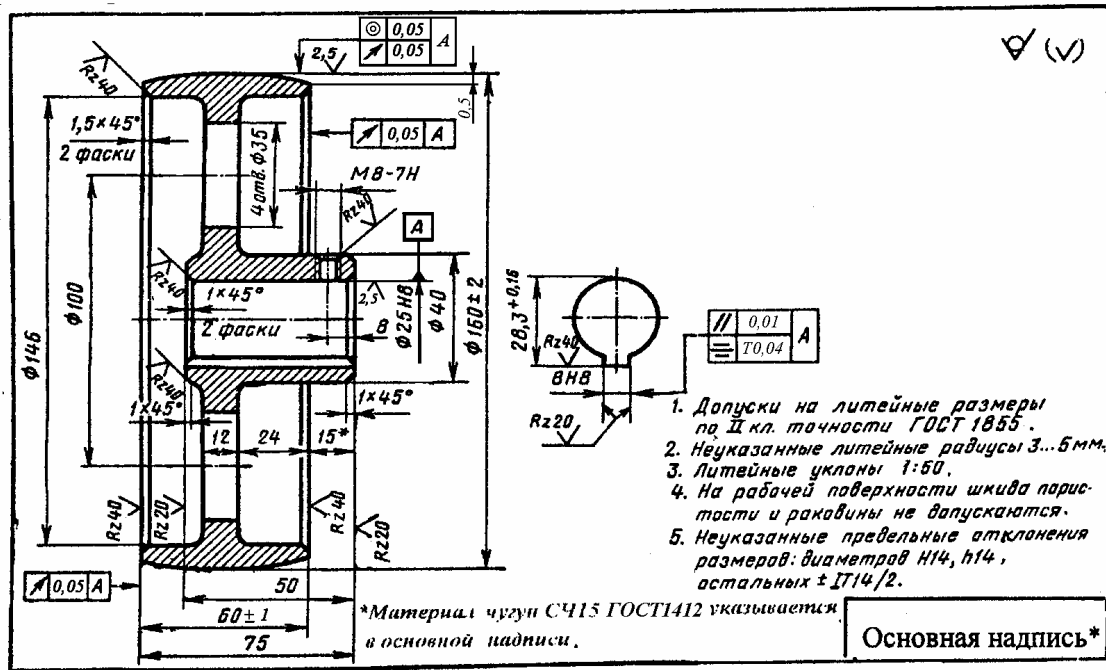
Рабочий чертеж шкива для плоского ремня
